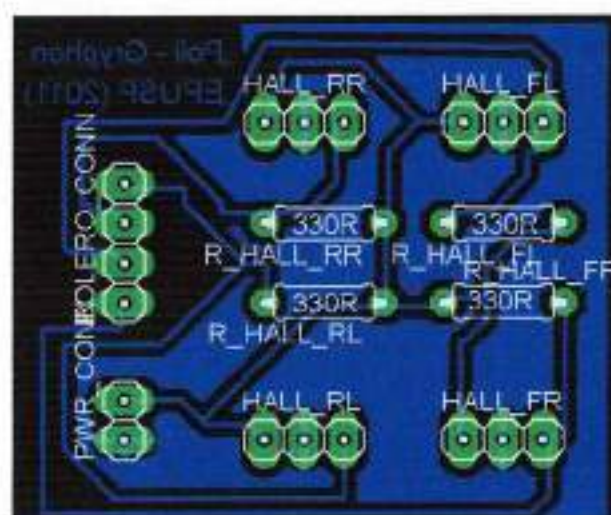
Desenho do Circuito Impresso de Controle dos Motores
